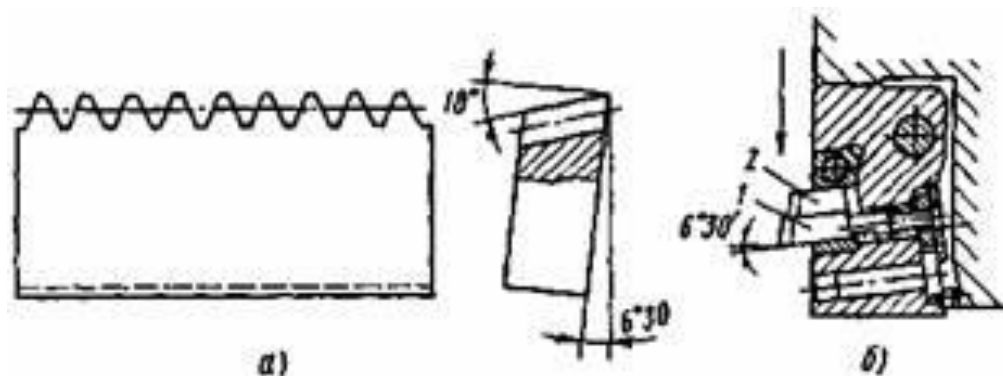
Зубчатая гребенка (а) и ее закрепление в суппорте станка (б)
